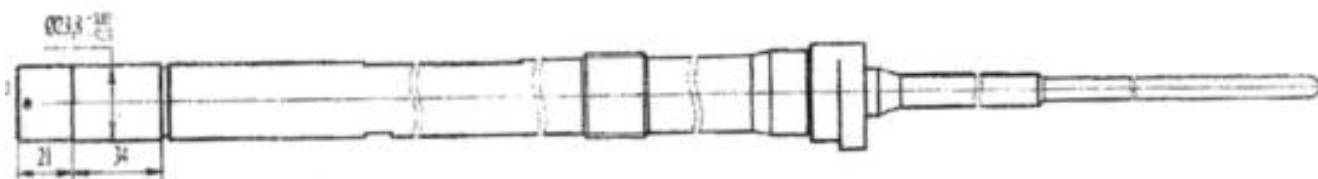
Габаритне креслення БДПЗ-Р-5.01-25
